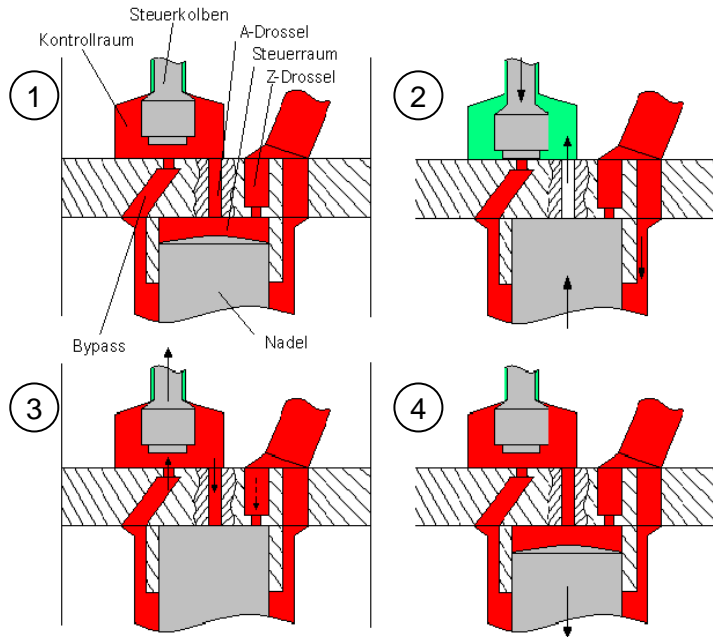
Hydrauliksystem aktueller Piezo-Injektoren
